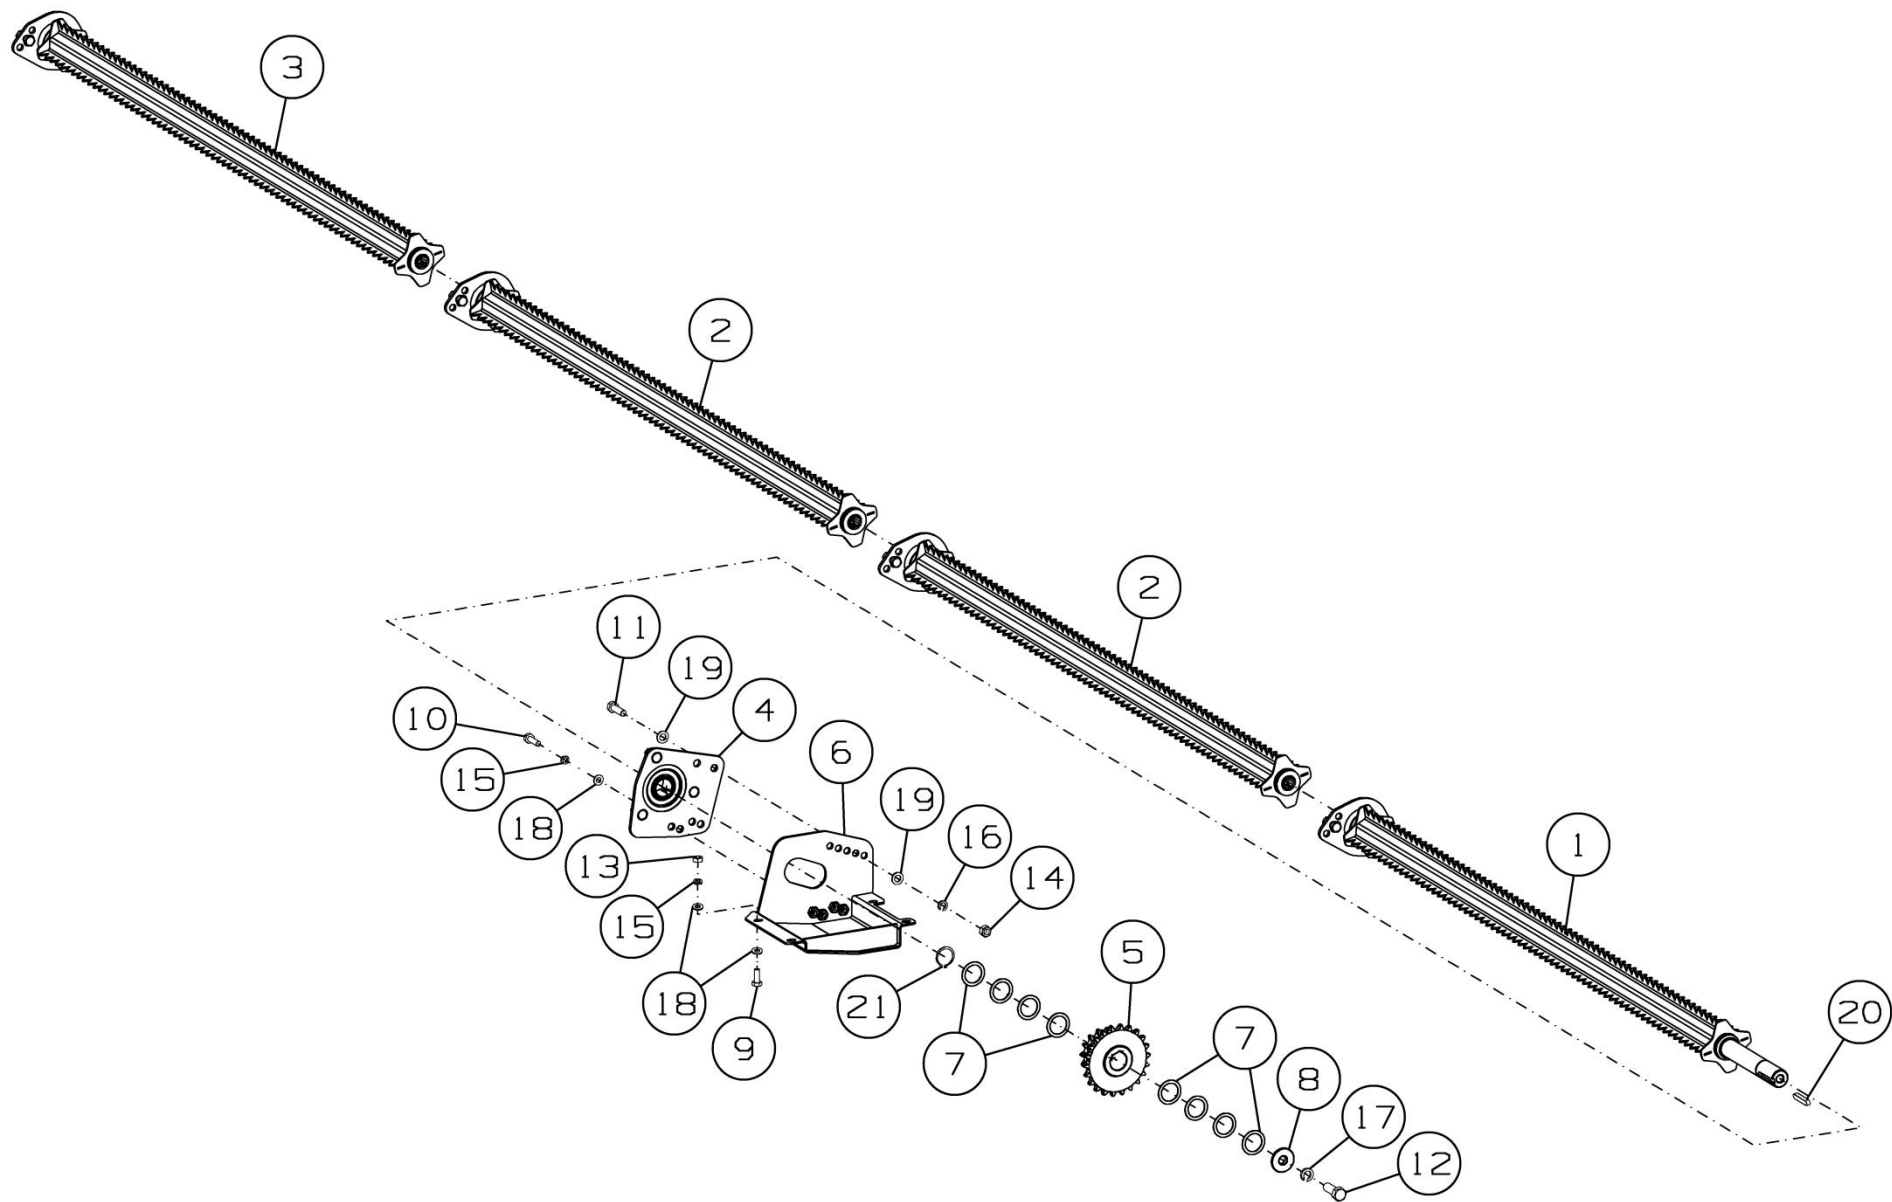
Вал протягивающий SS-780.01.06.000-05
